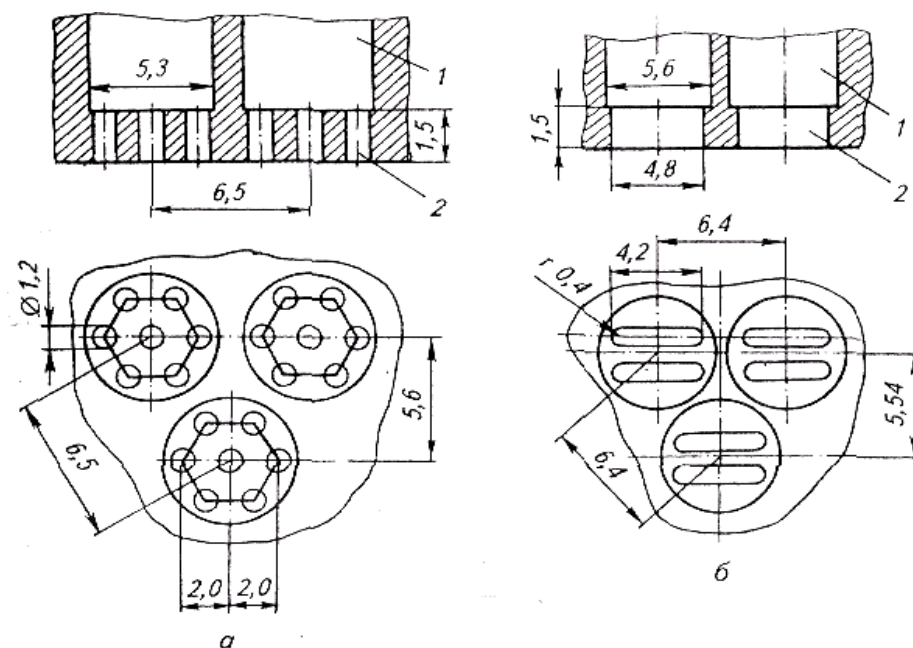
Профили отверстий в матрице без вкладышей: а – для вермишели; б – для лапши
